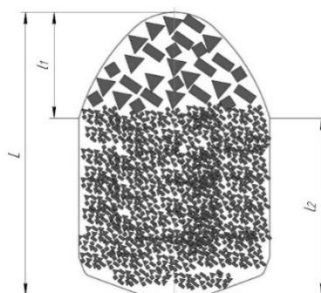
Ріжуча вставка спеціальної конструкції з металокерамічного сплаву:
